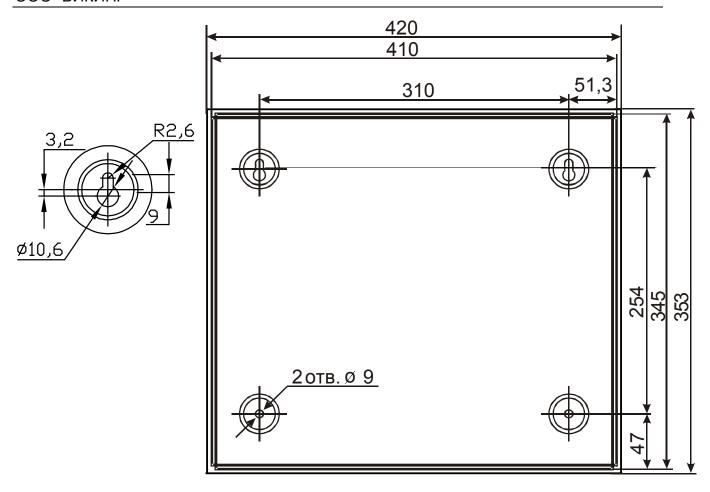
Присоединительные размеры ИБП 1200/2400 исп. 2
